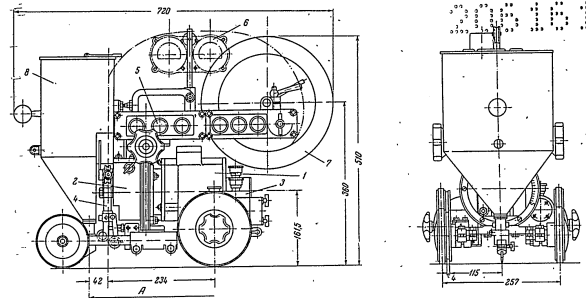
Чертеж общего вида сварочного трактора TC-17-M; А — направление движения трактора
